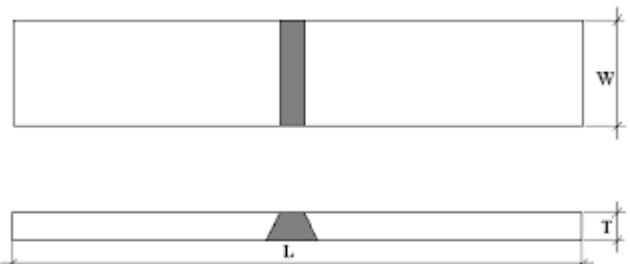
Dimensi dan ukuran spesimen untuk uji lengkung
